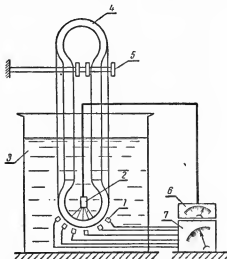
Схема дефектовки покрышки на высокочастотной ультразвуковой установке:
